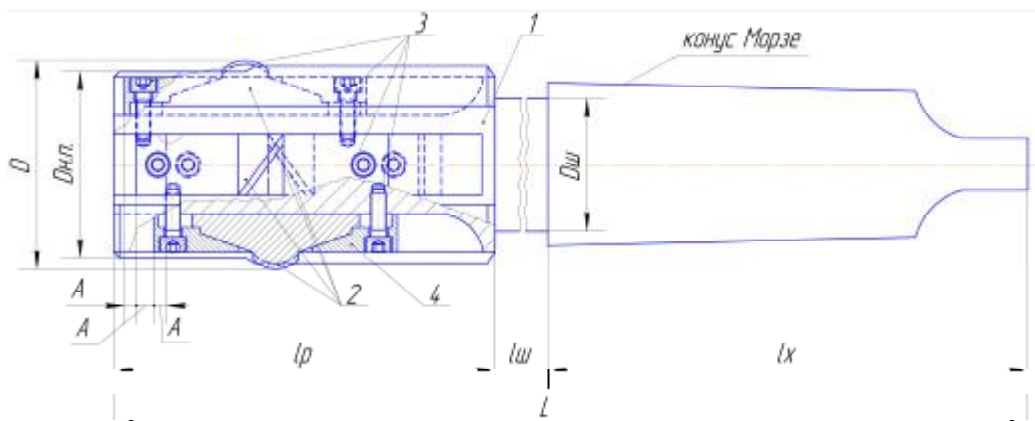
Конструкция резцовой сборной развёртки с безвершинными зубьями, общий вид
